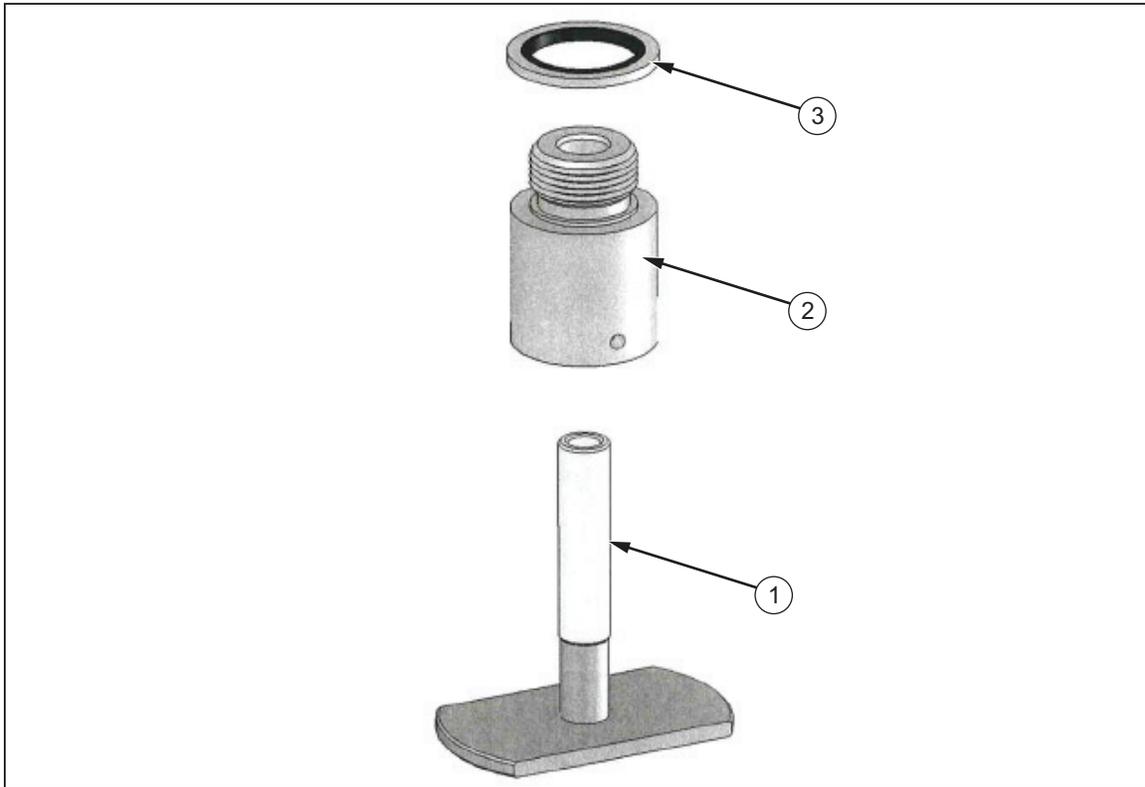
KZE-Baugruppe – 10 mm – Unterdruck
